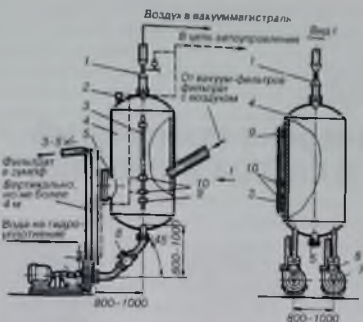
Схема установки ресивера и центробежных насосов, откачивающих фильтрат из вакуум-ресивера:
